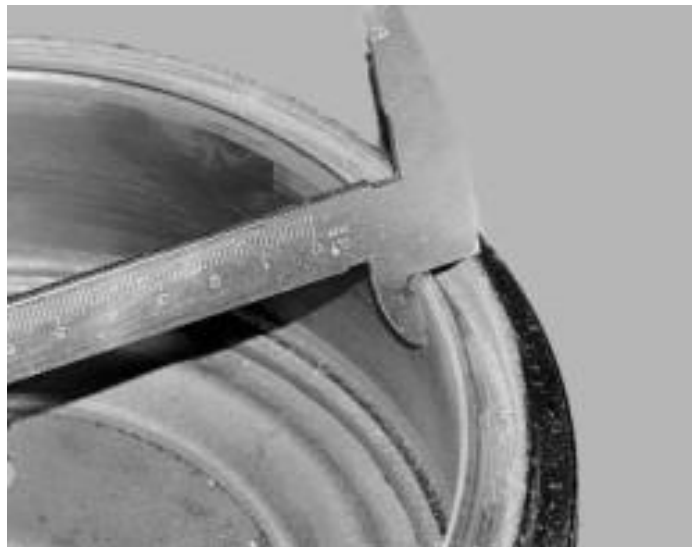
Вимірювання діаметра робочої поверхні гальмівного барабана
